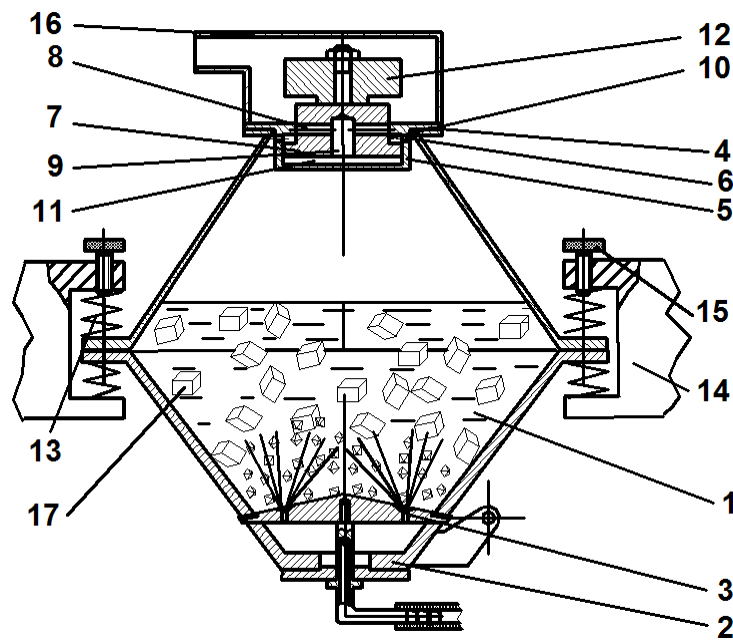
Установка для абразивної обробки дрібних деталей
